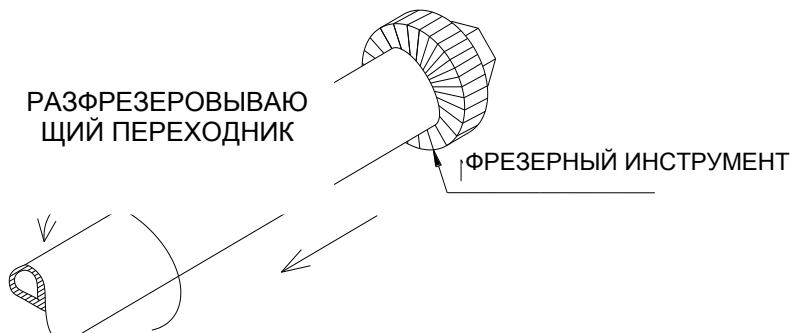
Обработка торца посадочной поверхности на недоступной иным способом навариваемой детали
